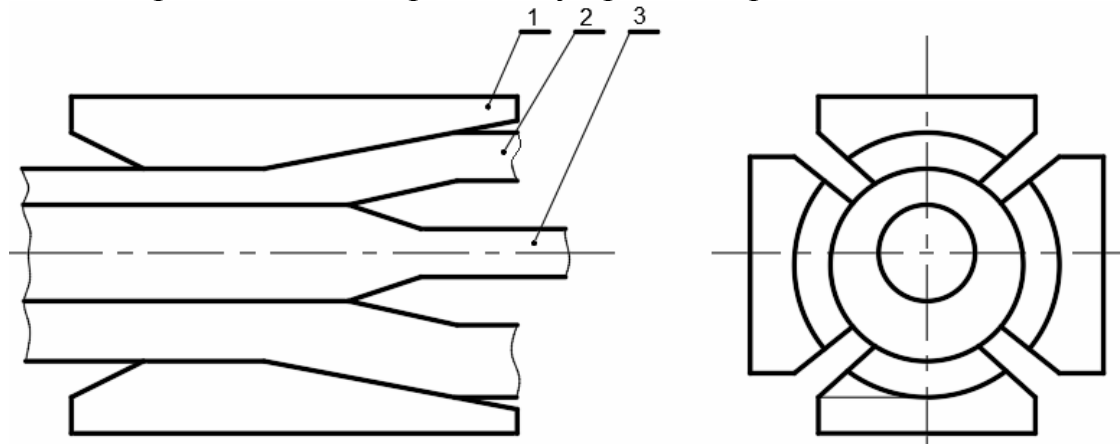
Схема радиального обжатия эксцентричной заготовки: 1 – боек; 2 – заготовка; 3 – оправка
